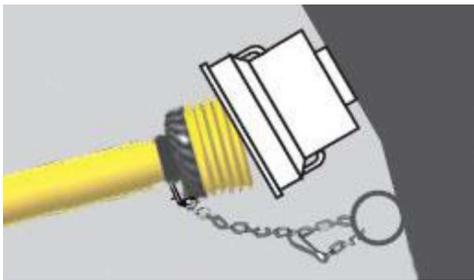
Befestigung des Zapfwellenrohrs mit einer Kette.
